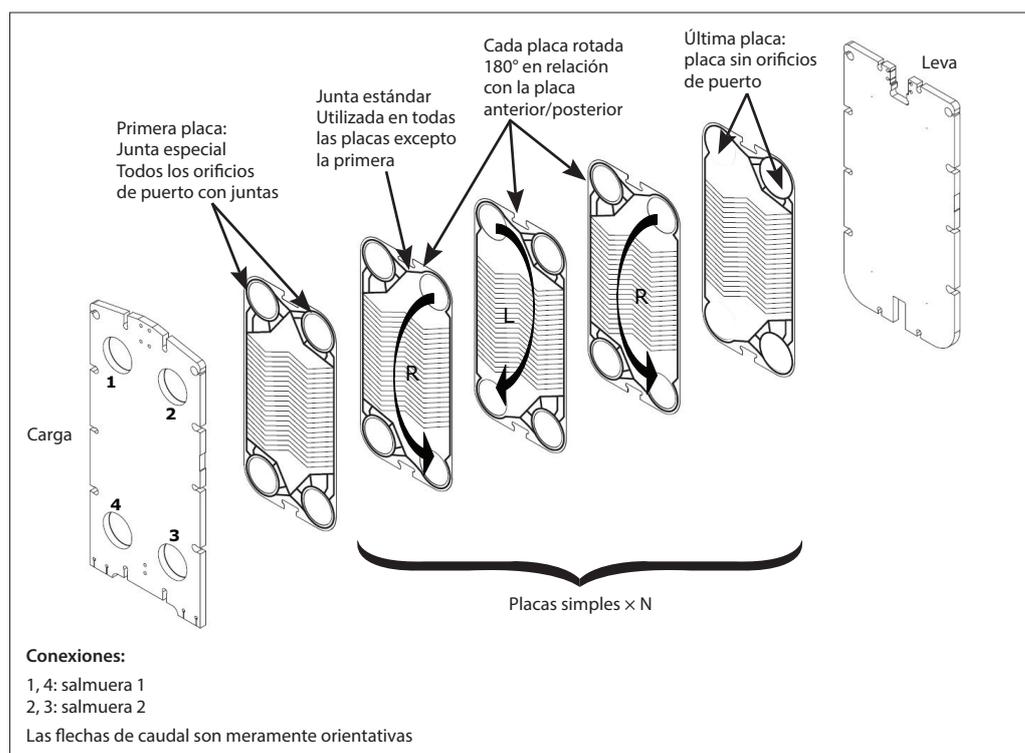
Placas simples: placas izquierdas y derechas y caudal
